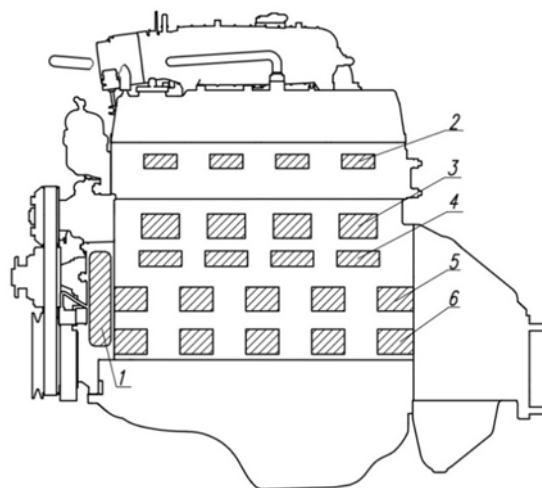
Зоны прослушивания двигателя. 1-шестерен распределительных; 2-клапанов; 3-пальцев поршневых; 4, 5-толкателей, штанг клапанов, подшипников распределительного вала; 6-подшипников коренных коленчатого вала.
